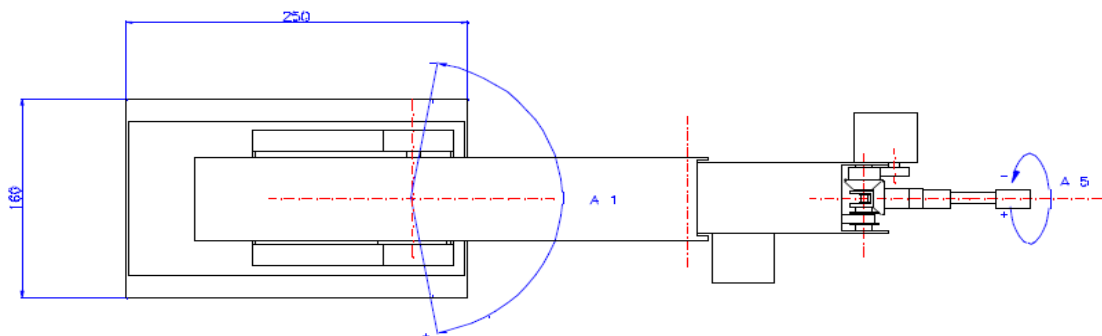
Les dimensions du robot ROB3(vue de haut)
